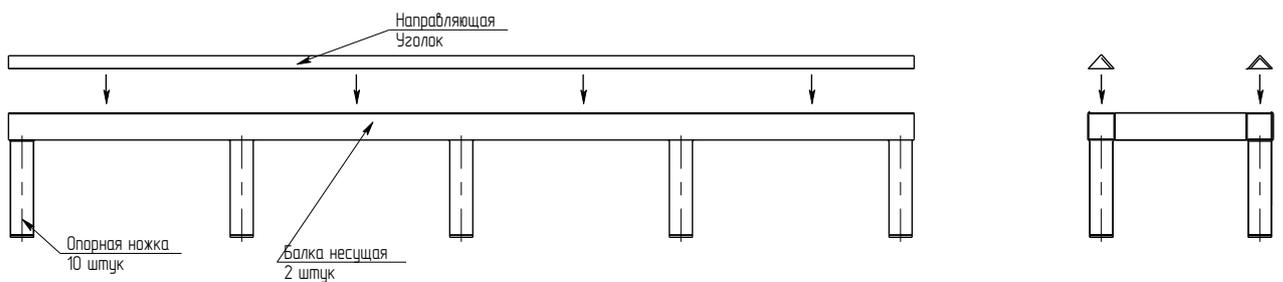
Соединение рамы с опорной ножкой с помощью сварки
